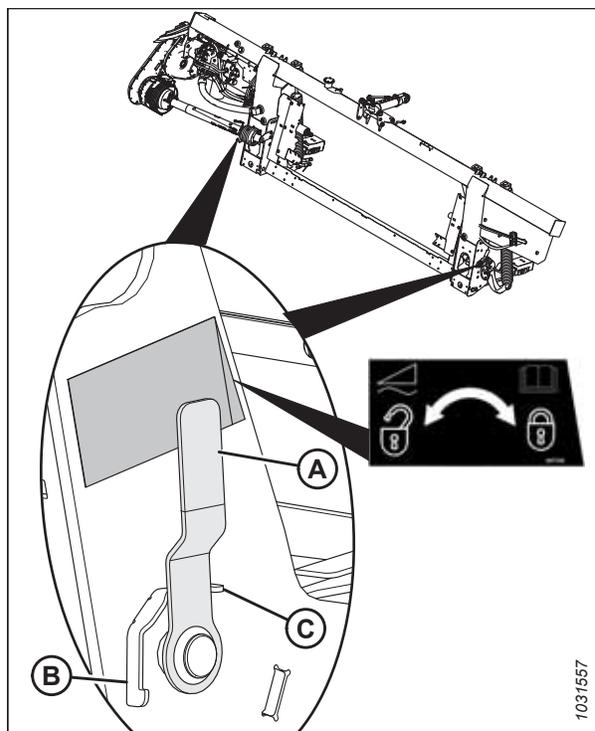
Dispositivo di bloccaggio flottazione – in posizione bloccata
